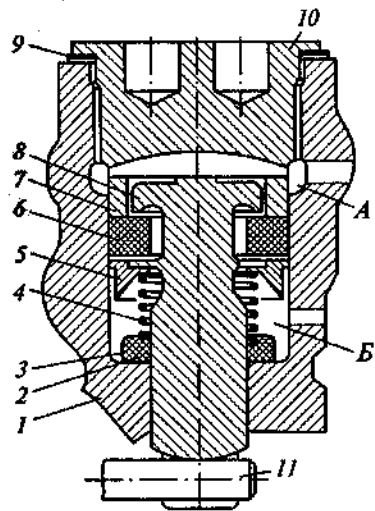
Регулятор тормозных сил легкового автомобиля ВАЗ: 1 — корпус; 2 — кольцо; 3 — обойма; 4 — пружина; 5 — тарелка; 6 — уплотнитель; 7 — втулка; 8 — поршень; 9 — прокладка; 10 — пробка; 11 — торсион; А и Б — полости
